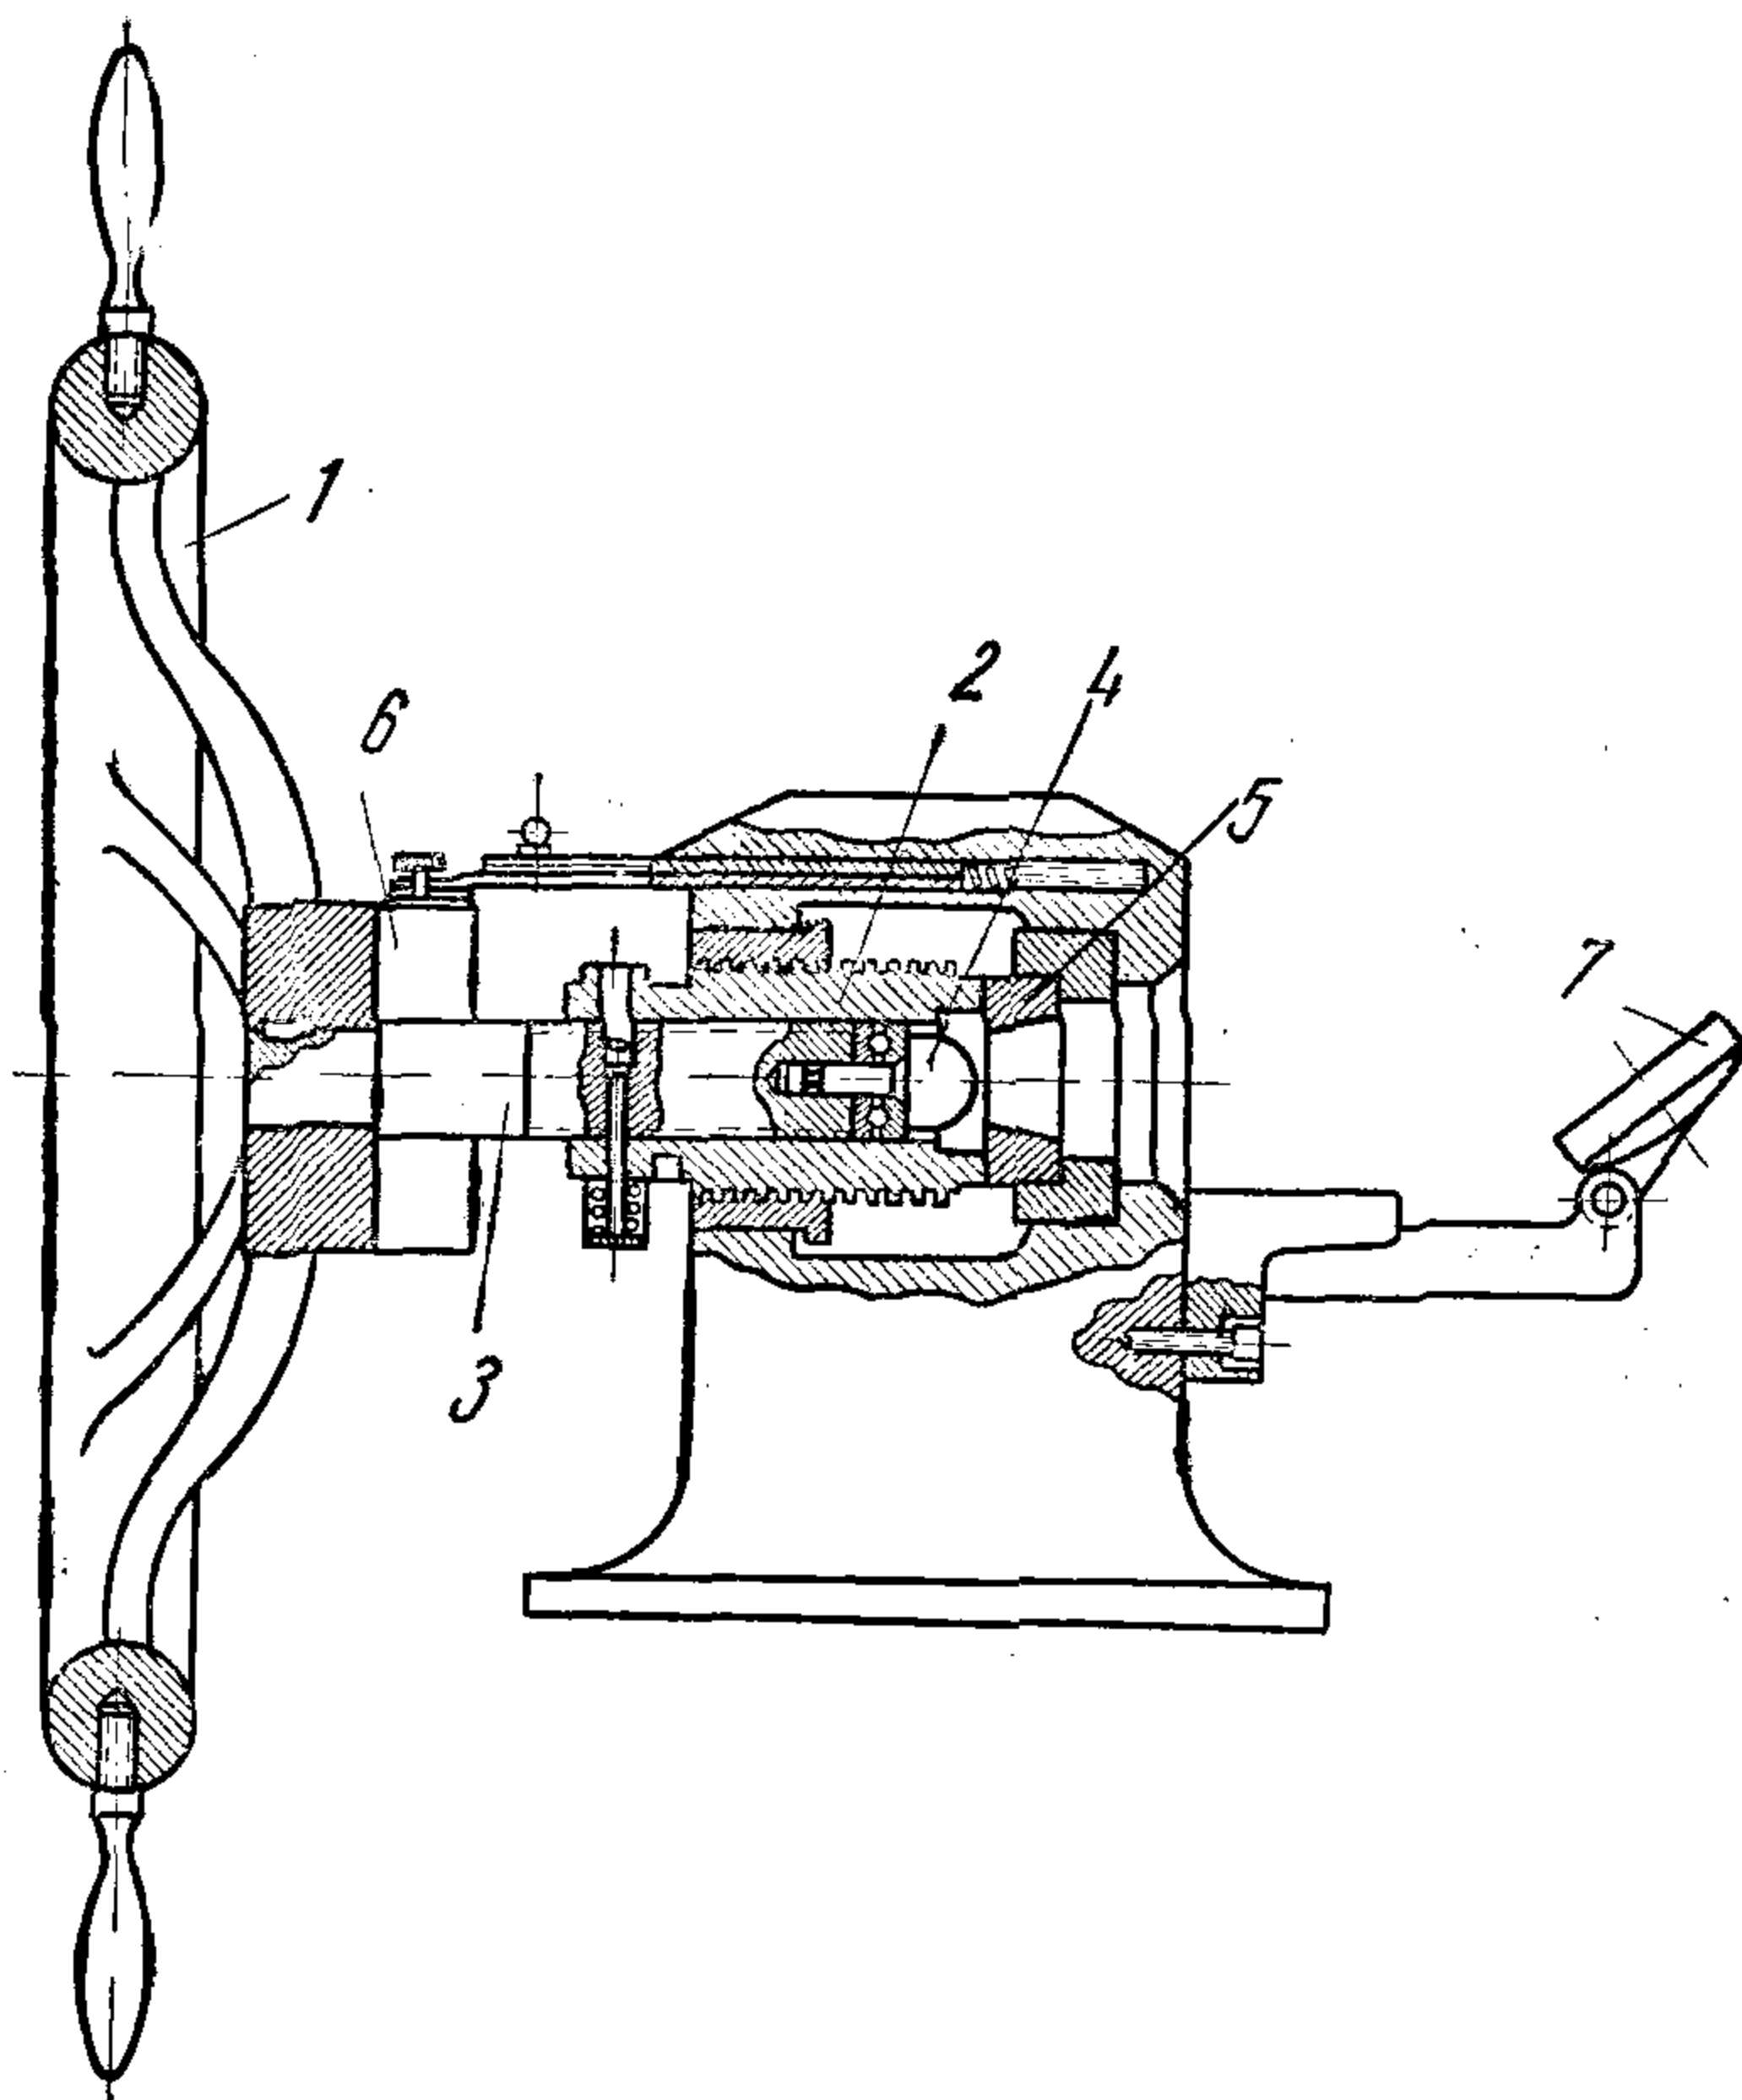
Схема прибора для испытания листового металла на выдавливание:
